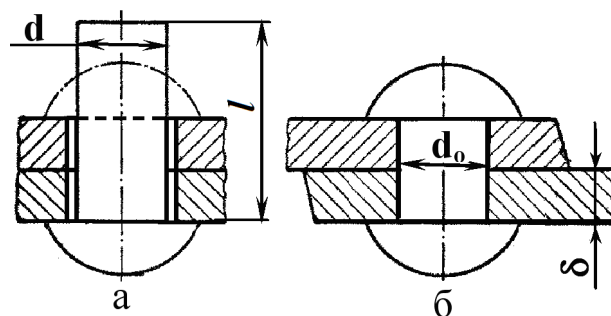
Технологія виготовлення заклепкового з'єднання
